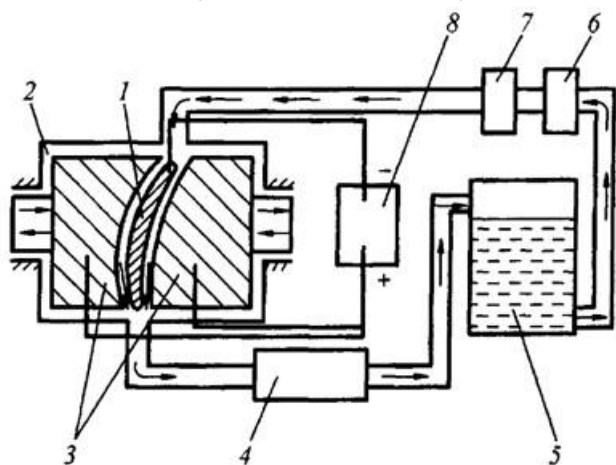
схема установки для ЕХО: 1 – робоча камера; 2 – лопатка; 3 – джерело струму; 4 – нагнітач; 5 – теплообмінник; 6 – бак з електролітом; 7 – центрифуга; 8 – електроди (інструменти).
